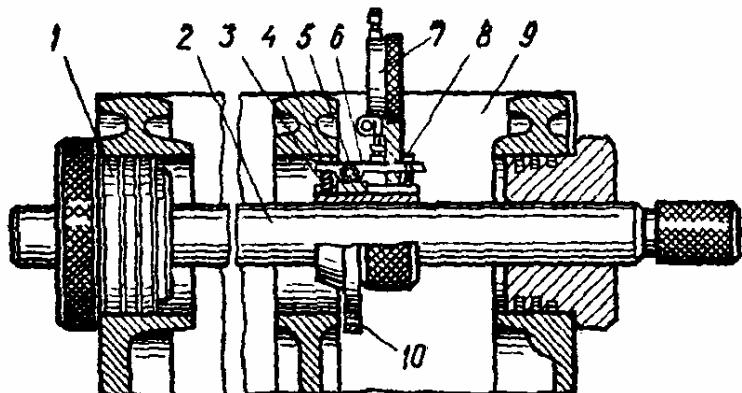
Пристосування для перевірки співвісності отворів у блок-картері під корінні підшипники: 1 - втулка; 2 - оправка; 3 - пружина; 4 - сферичний палець; 5 - вісь; 6 - важіль; 7 - індикатор годинного типу; 8 - регулювальний гвинт; 9 - блок; 10 - упорний штифт
